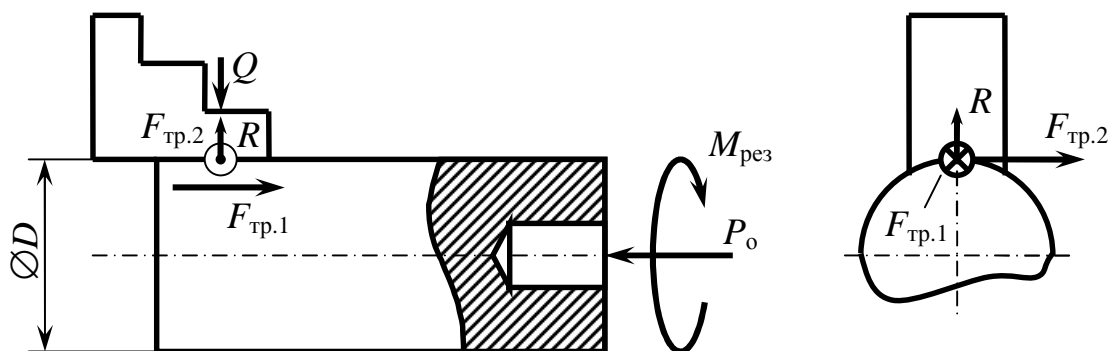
Схема к определению силы закрепления заготовки при сверлении отверстия на токарном станке
